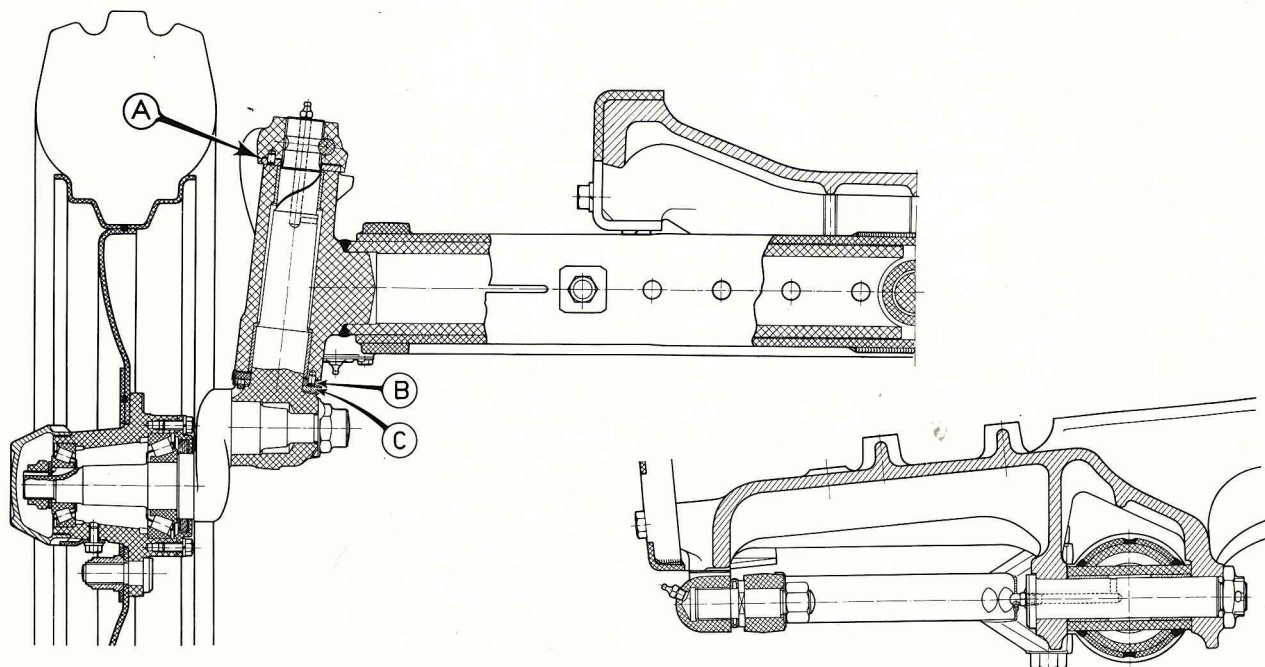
Sezione longitudinale sull'assale anteriore e ruote direttrici e sezione sul perno di incernieramento.
